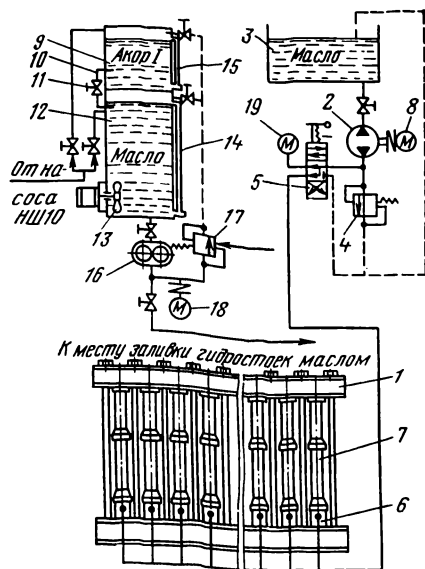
Стенд для испытания индивидуальных гидростоек
